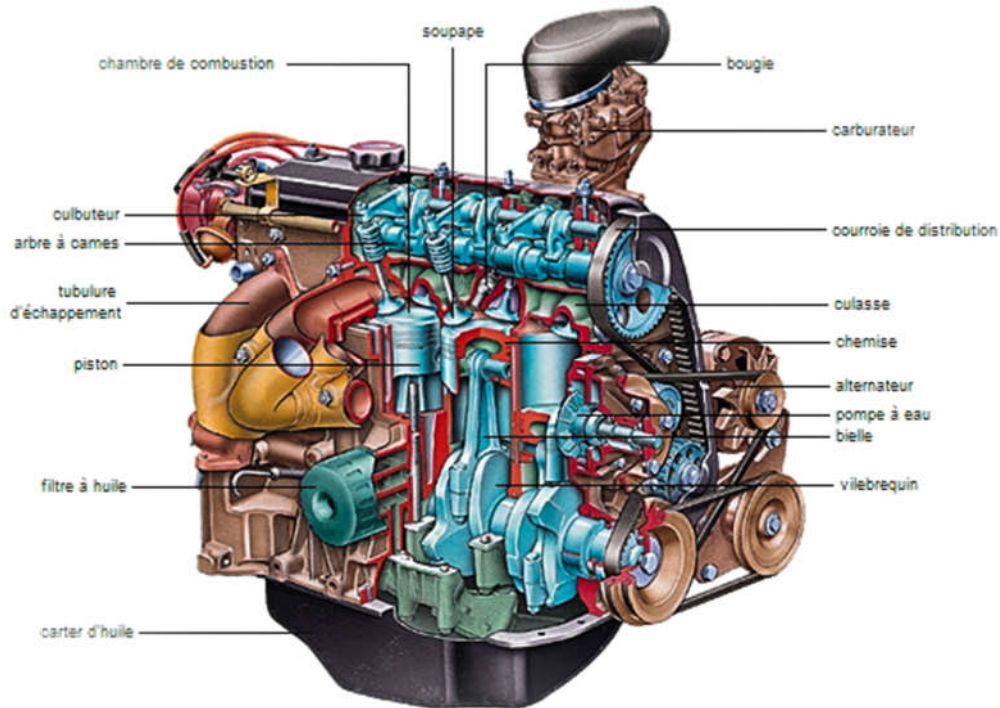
Vue éclatée d'un moteur à explosion [2].
